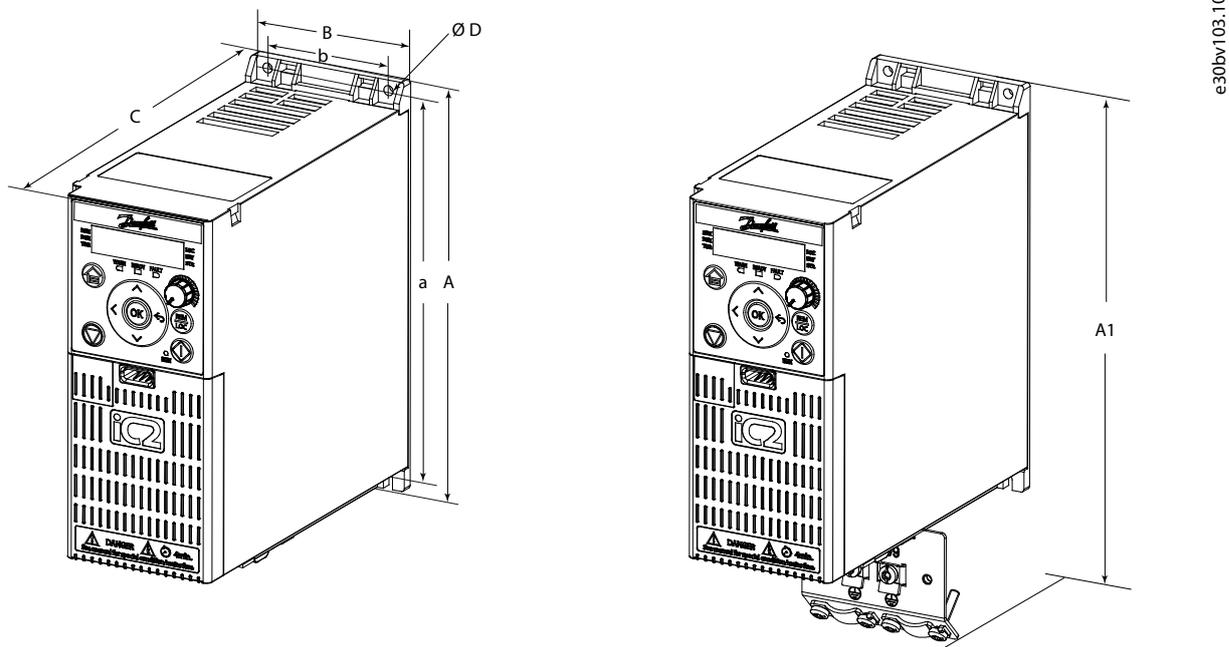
Размеры и габариты корпусов IP20/открытого типа
